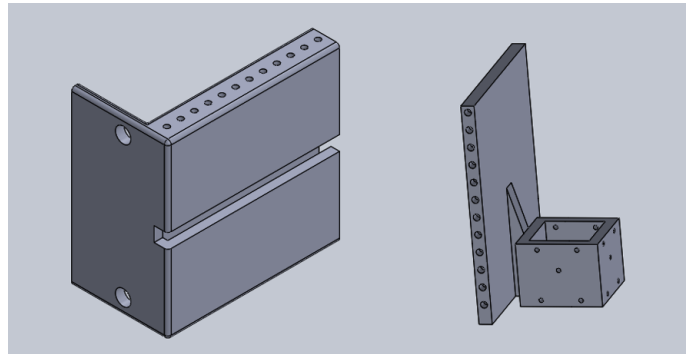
Piezas del soporte diseñado para sostener la cámara
